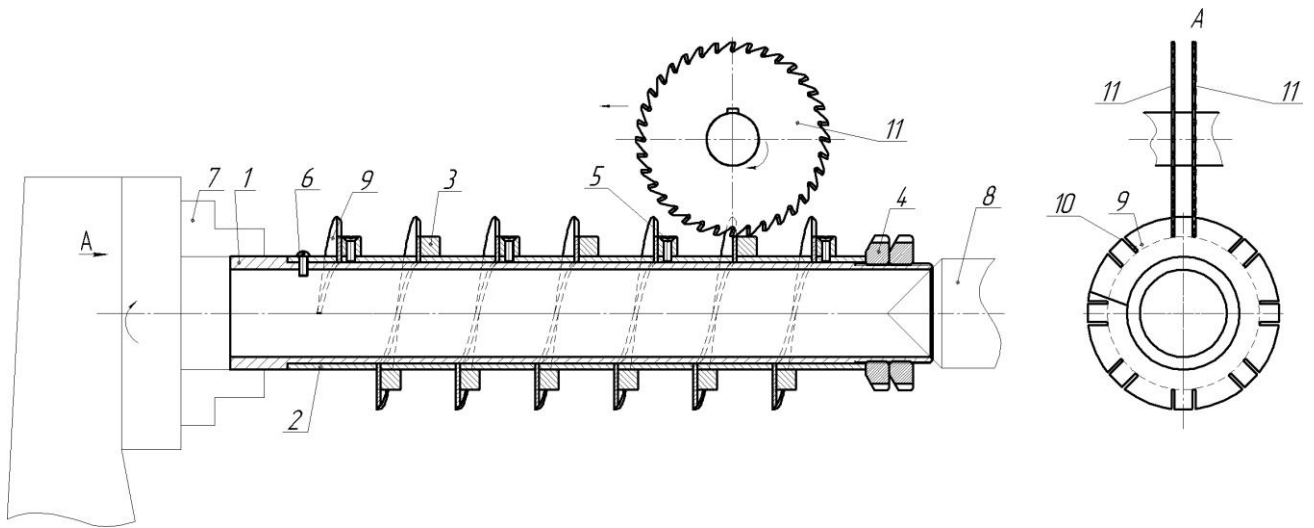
Схема процесу фрезерування пазів на тонкостінних витках гвинтових заготовок [25]
